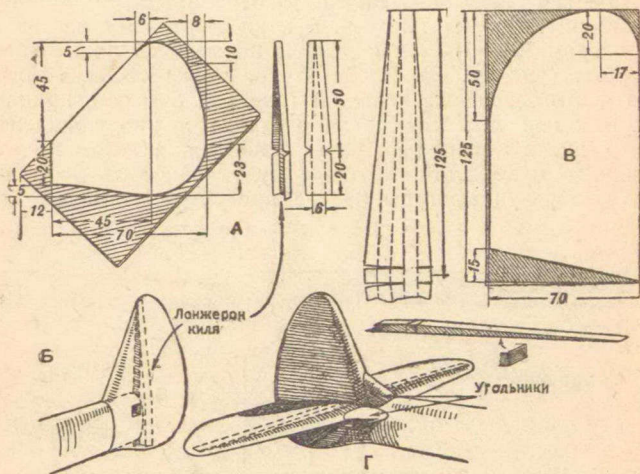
Изготовление хвостового оперения: А — киль и лонжерон кия, Б — крепление кия к фюзеляжу, В — стабилизатор, Г — крепление стабилизатора и общий вид хвостового оперения.
